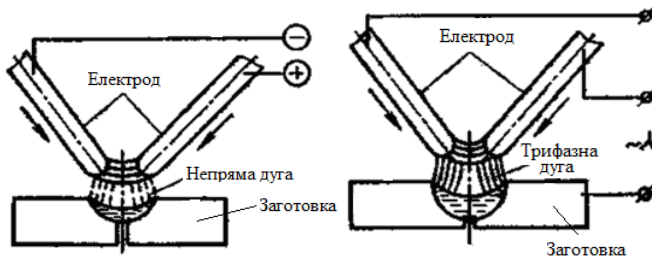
Зварювання непрямою дугою, трифазною дугою
